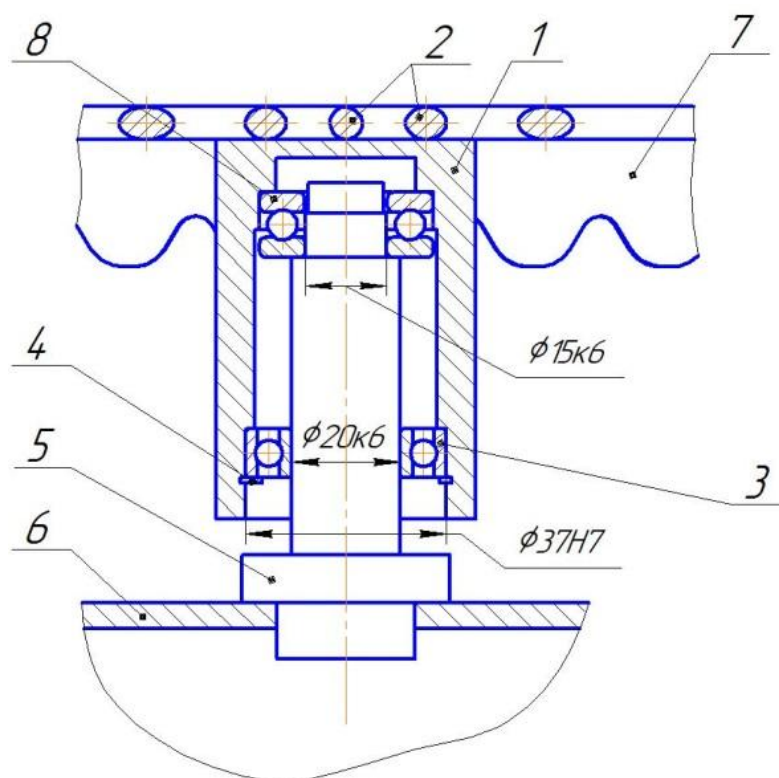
Компоновочная схема модернизированной установки для мойки агрегатов
